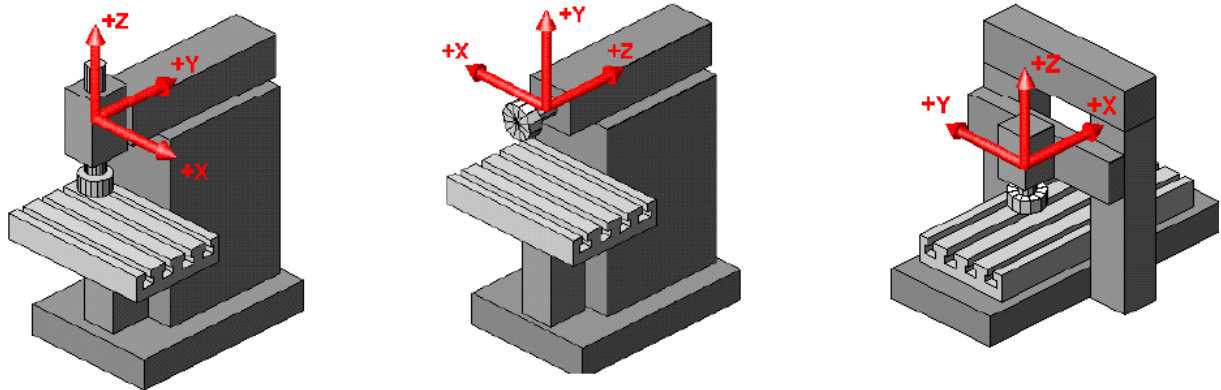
Disa shembuj të përcaktimi të kahjeve te makinat frezuese CNC. [2]
